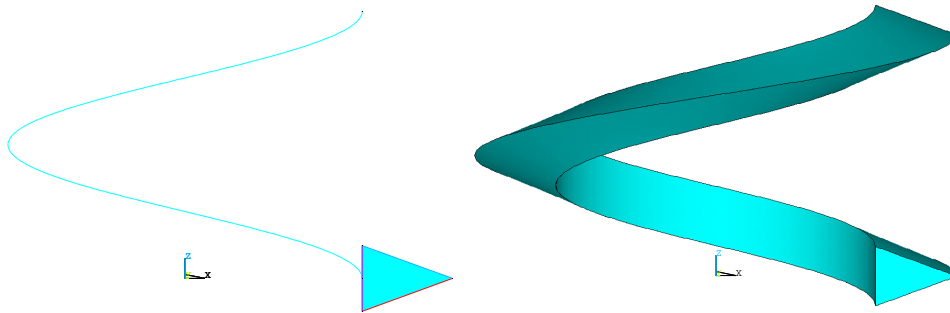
links: Spirale mit Gewindequerschnitt, rechts: extrudiertes Gewinde
